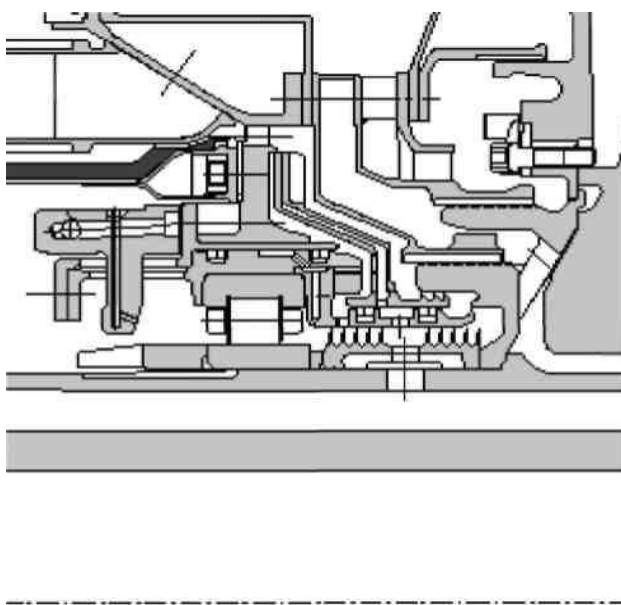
Задня опора ротора ВД з роликопідшипником
